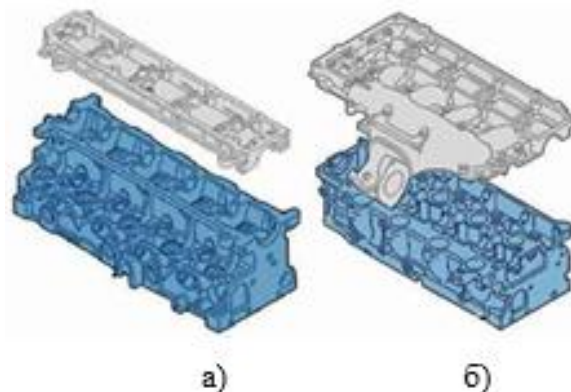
а) – схема 8-клапанної головки блоку циліндрів;
